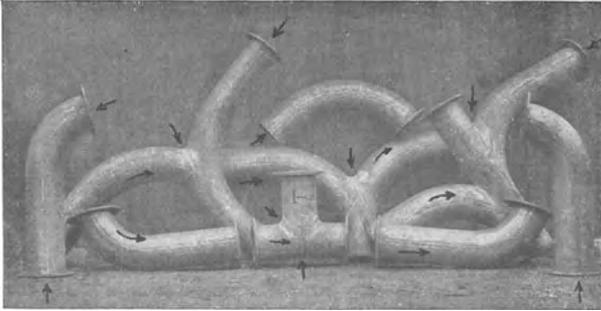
Gruppe geschweißter Kupferrohr-Formstücke.
